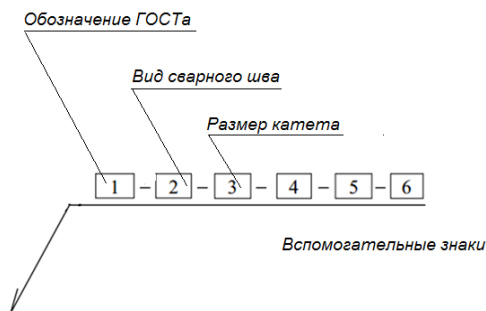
Пример обозначения сварного шва на чертежах
